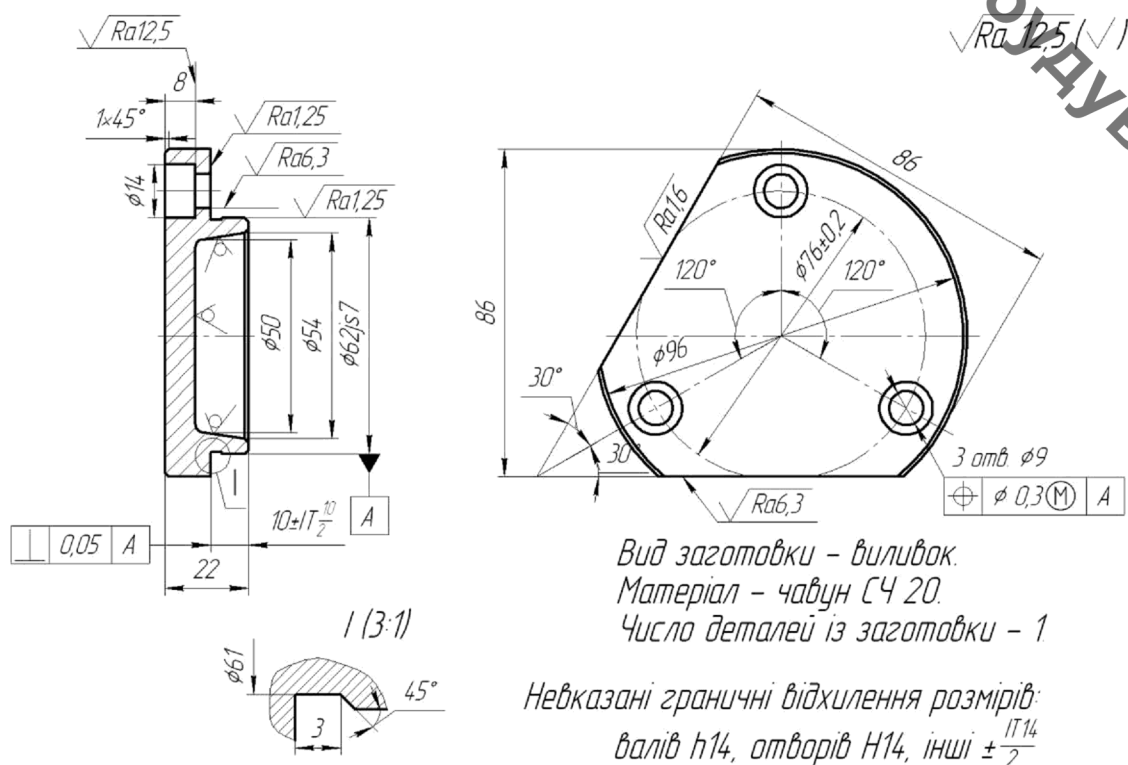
Ескіз типової деталі типу "Фланець"
